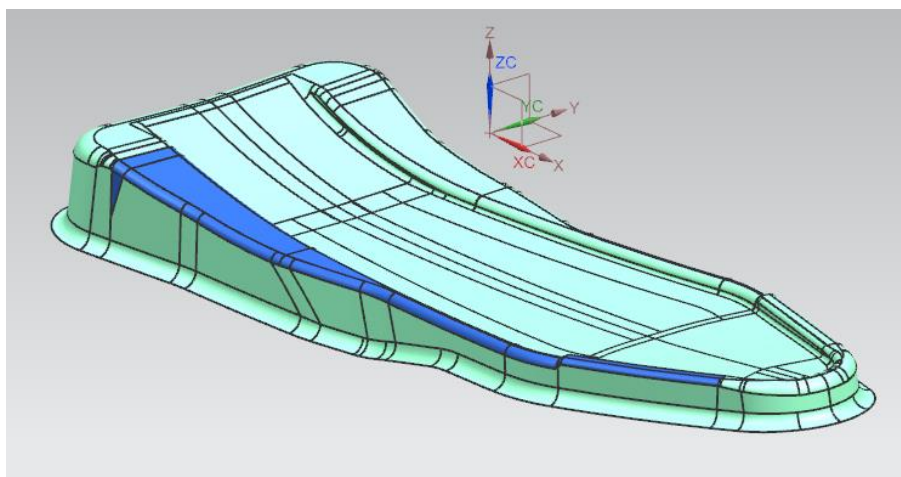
Модель для нахождения формы и размеров исходной заготовки
